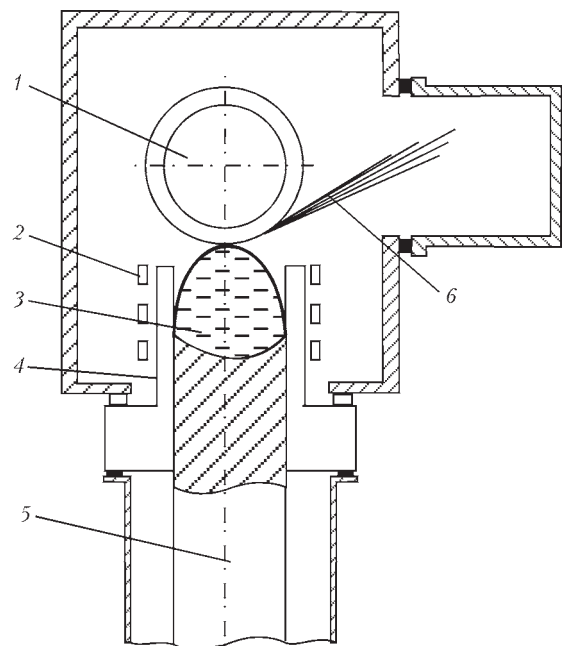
Схема установки диспергирования из расплава: 1 — закалочный диск; 2 — индуктор; 3 — расплавленная ванна металла; 4 — секционный кристаллизатор; 5 — переплавляемая заготовка; 6 — быстрозакаленные чешуйки
